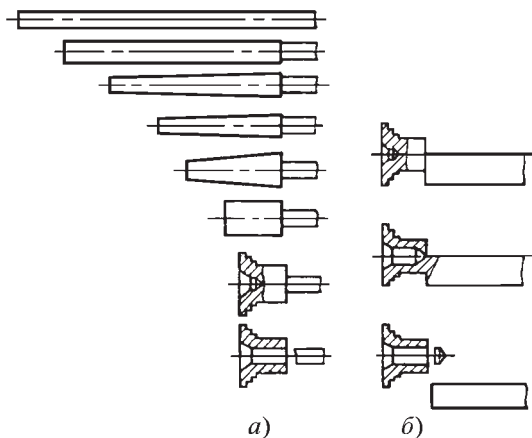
Варианты высадки поковки втулки из заготовок с различными исходными диаметрами
